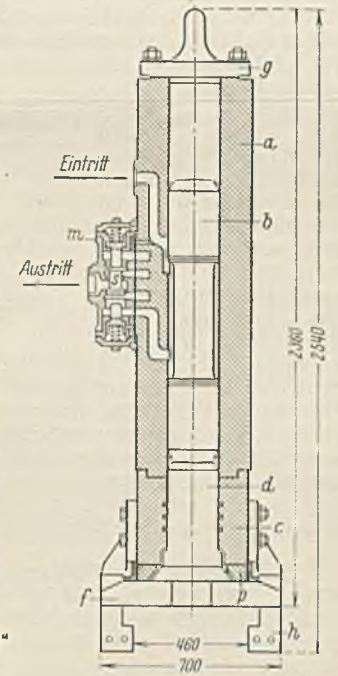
Schnitt durch die Druckluftramme (Demag-Union). a Zylinder. b Schlagkolben. c Zwischenzylinder. d Zwischenkolben. f Rammblock. g Zylinderdeckel. h Untersatz. m Steuergehäuse. p Prellscheibe. s Expansionskolbenschieber.
